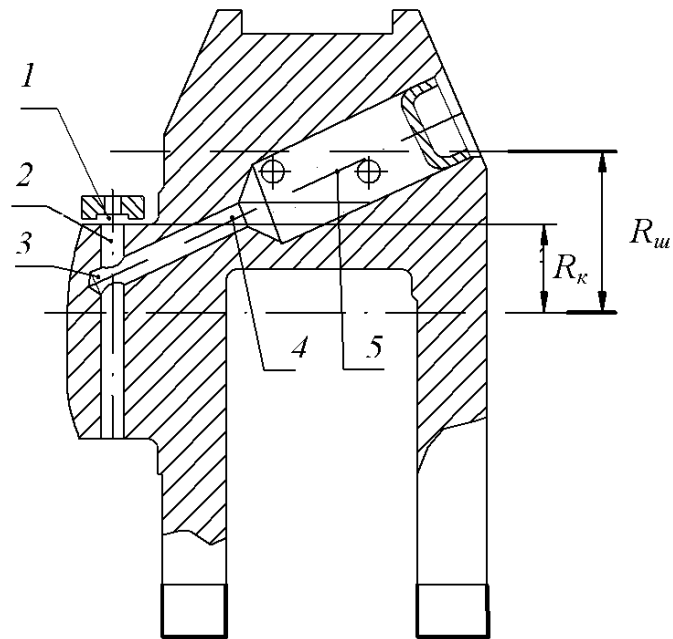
Схема смазки шатунного подшипника двигателя КамАЗ до изменения:
